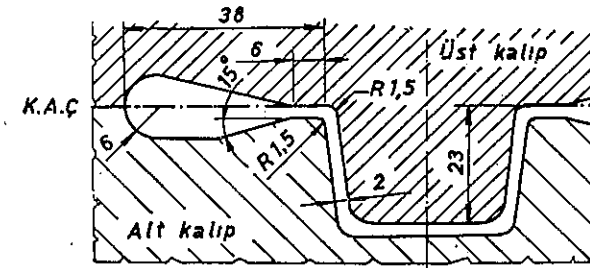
20 Büyük ve çok büyük boşluklu parçaların dövme işleminde kullanılan kalıpların çapak boşluğu ölçüleri
